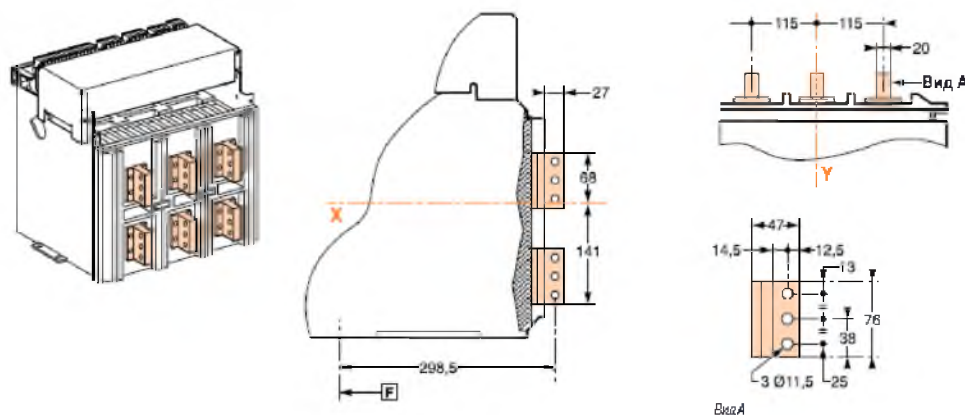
Горизонтальные и вертикальные выводы для заднего присоединения с присоединительными размерами для ВА–СЭЩ–АС08/10/12/16/20/25/32 выкатного исполнения
